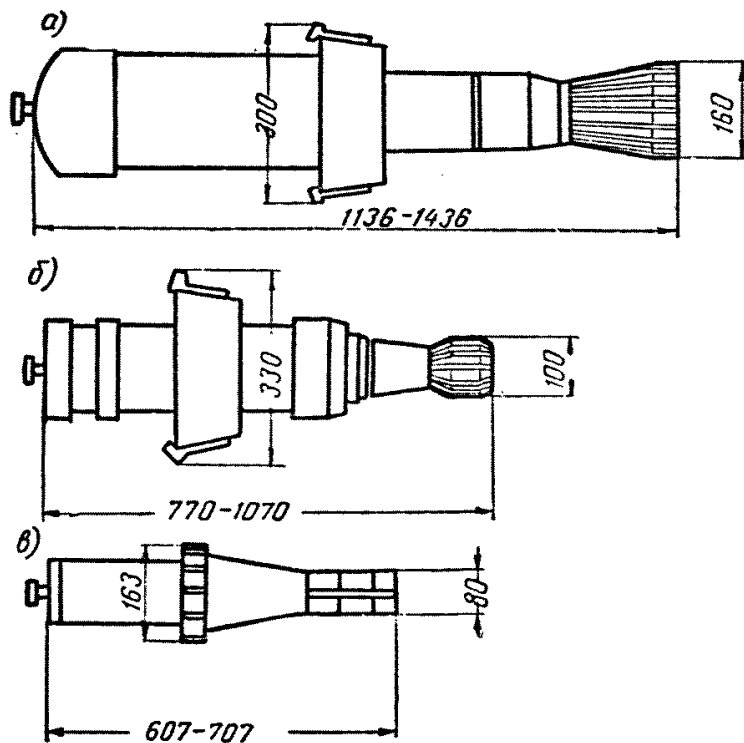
Габариты гидравлических домкратов двойного действия для натяжения пучковой арматуры
